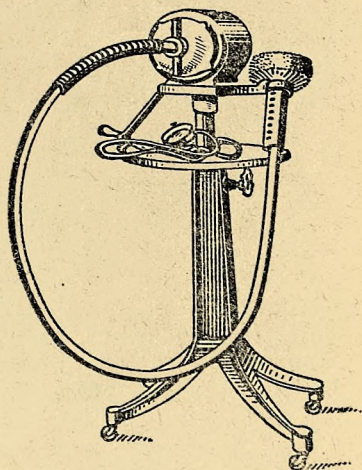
Шероховальный станок с гибким валом, укрепленный на стойке
